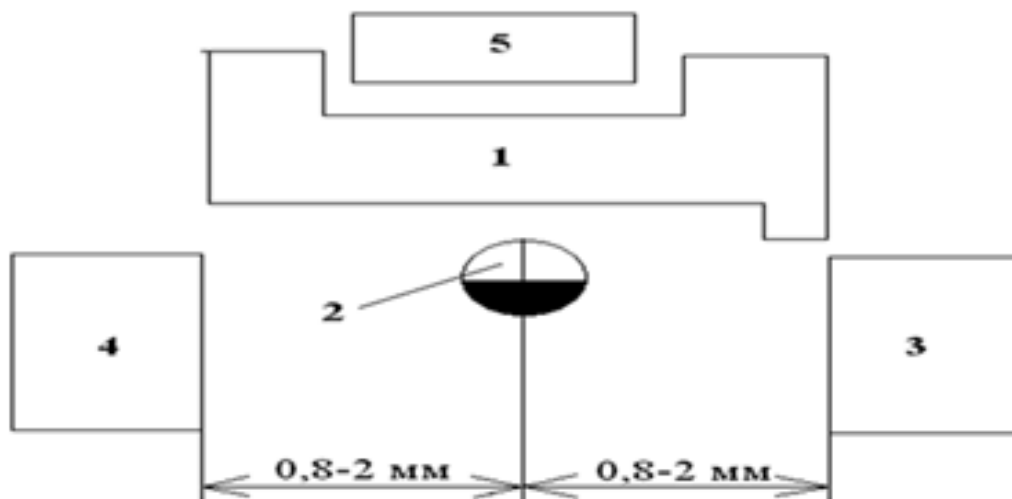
Схема планировки и организации рабочего места 1 – пресс; 2 – рабочий; 3 – стол для заготовок; 4 – стеллаж для деталей; 5 – ящик для отходов.
